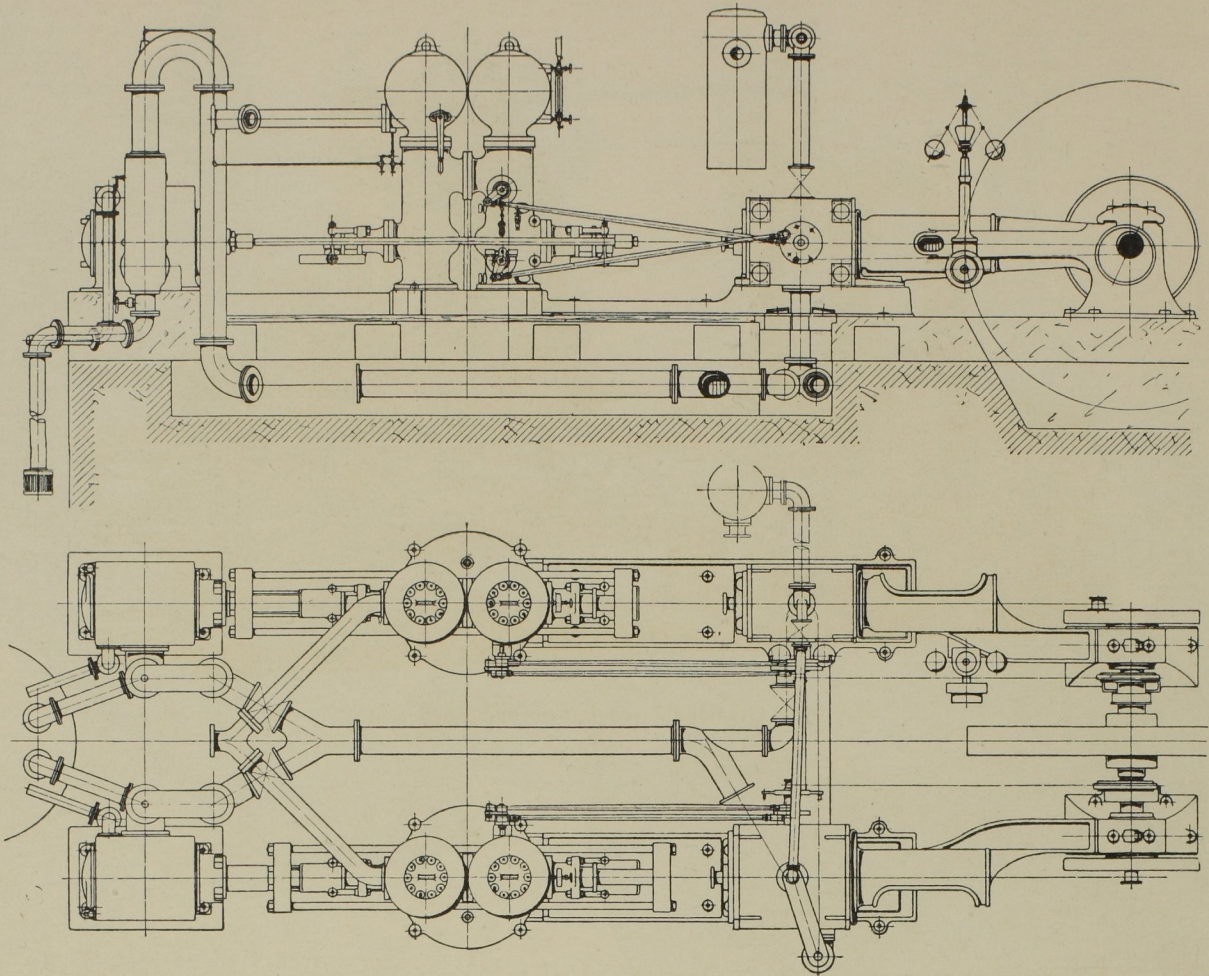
Seitenansicht und Grundriss. Masst. 1:64.
